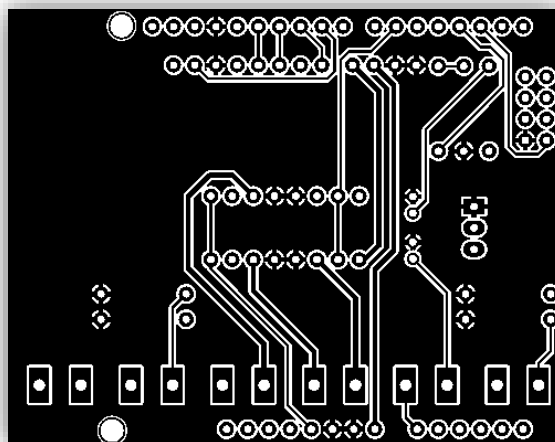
Diseño para impresión física capa inferior PCB, impresión – LockBikeRack
